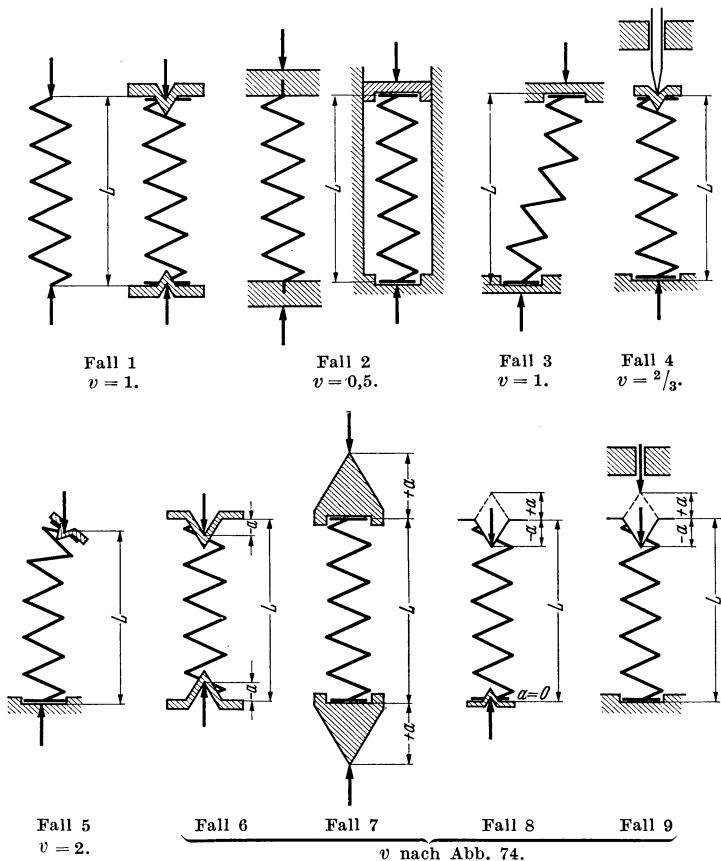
Die wichtigsten Fälle der Lagerung auf Knickung beanspruchter Schraubenfedern.
